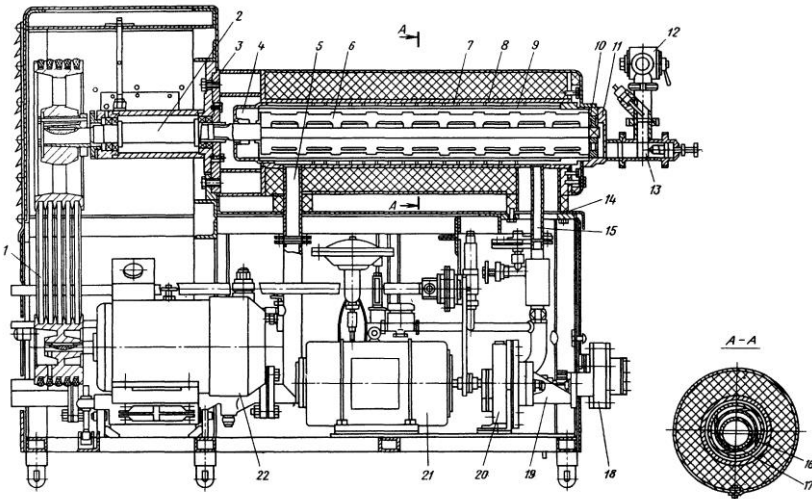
Загальний вид фризера марки Б6-ОФШ:
